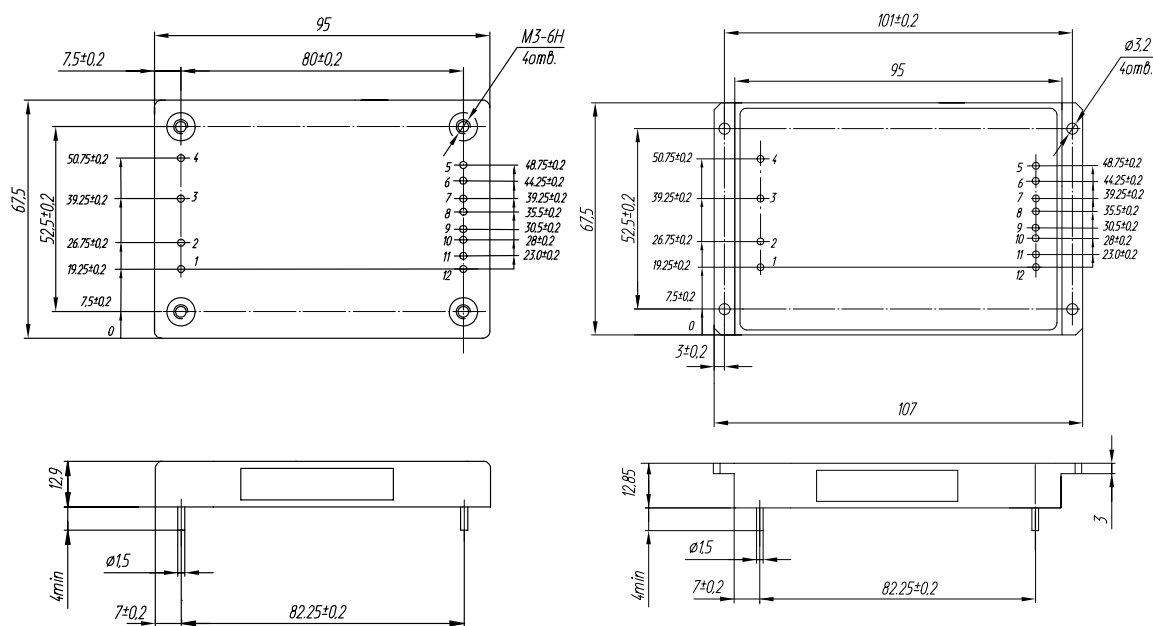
Габаритные чертежи модуля МДМ160-ЕП
